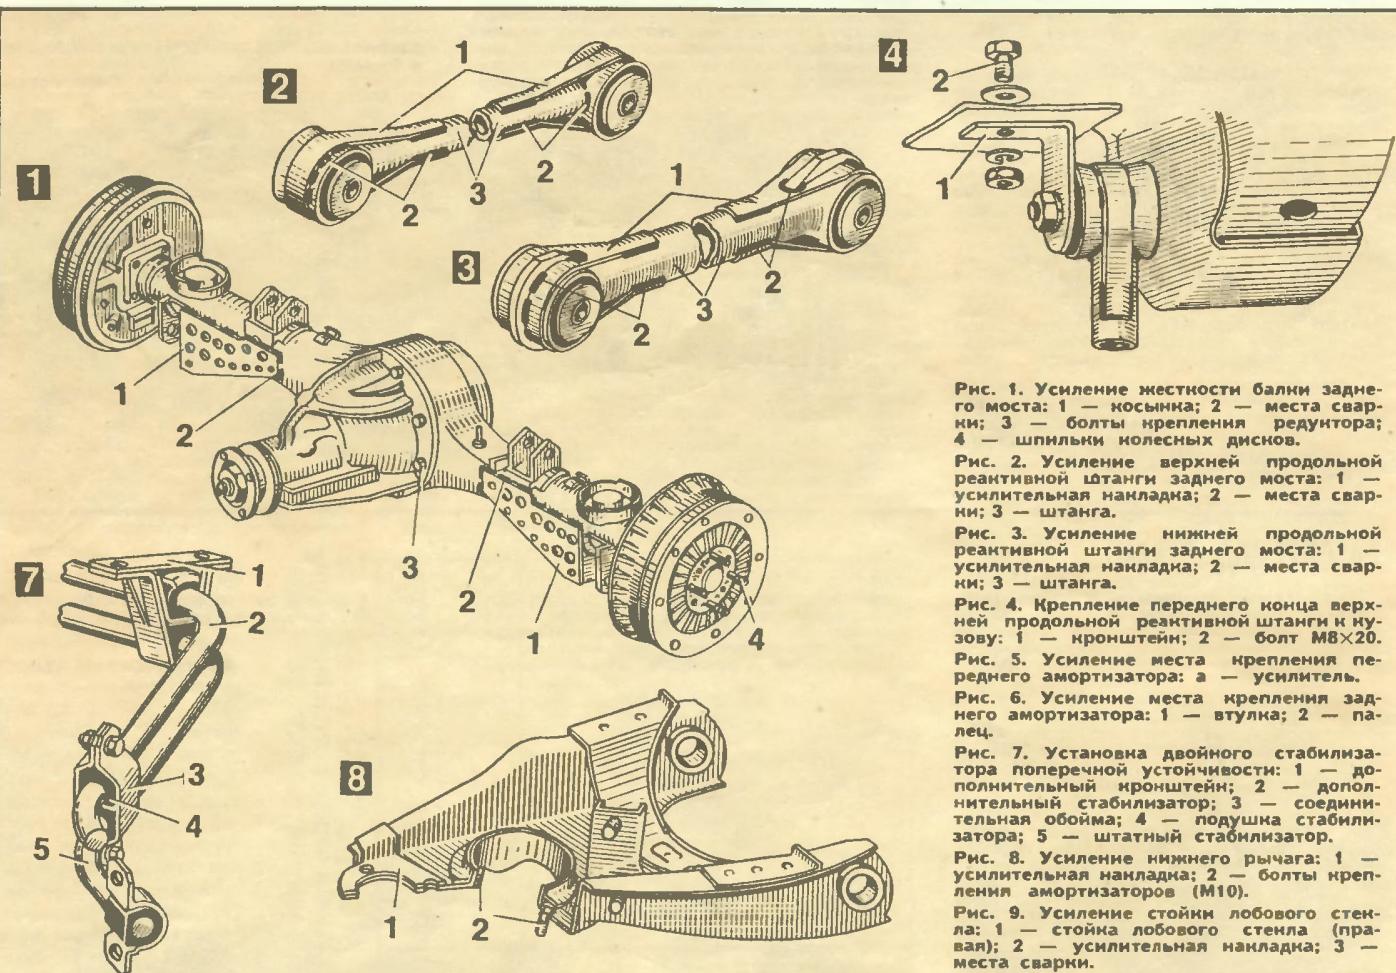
Усиление жесткости балки заднего моста: 1 — косынка; 2 — места сварки; 3 — болты крепления редуктора; 4 — шпильки колесных дисков.
